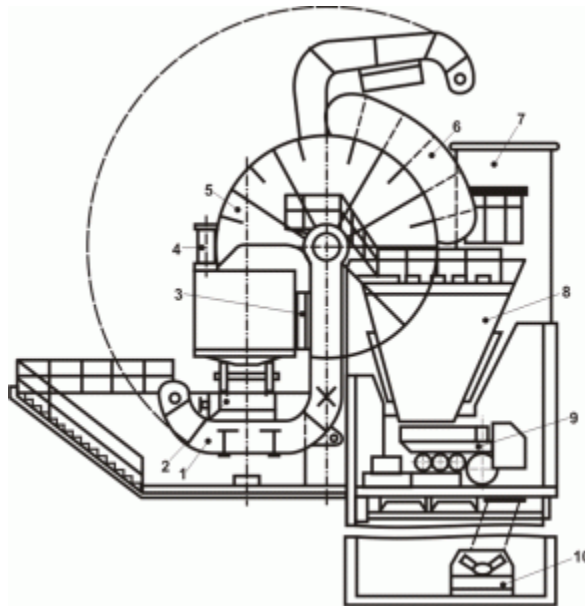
Боковой подъемно-поворотный вагоноопрокидыватель
